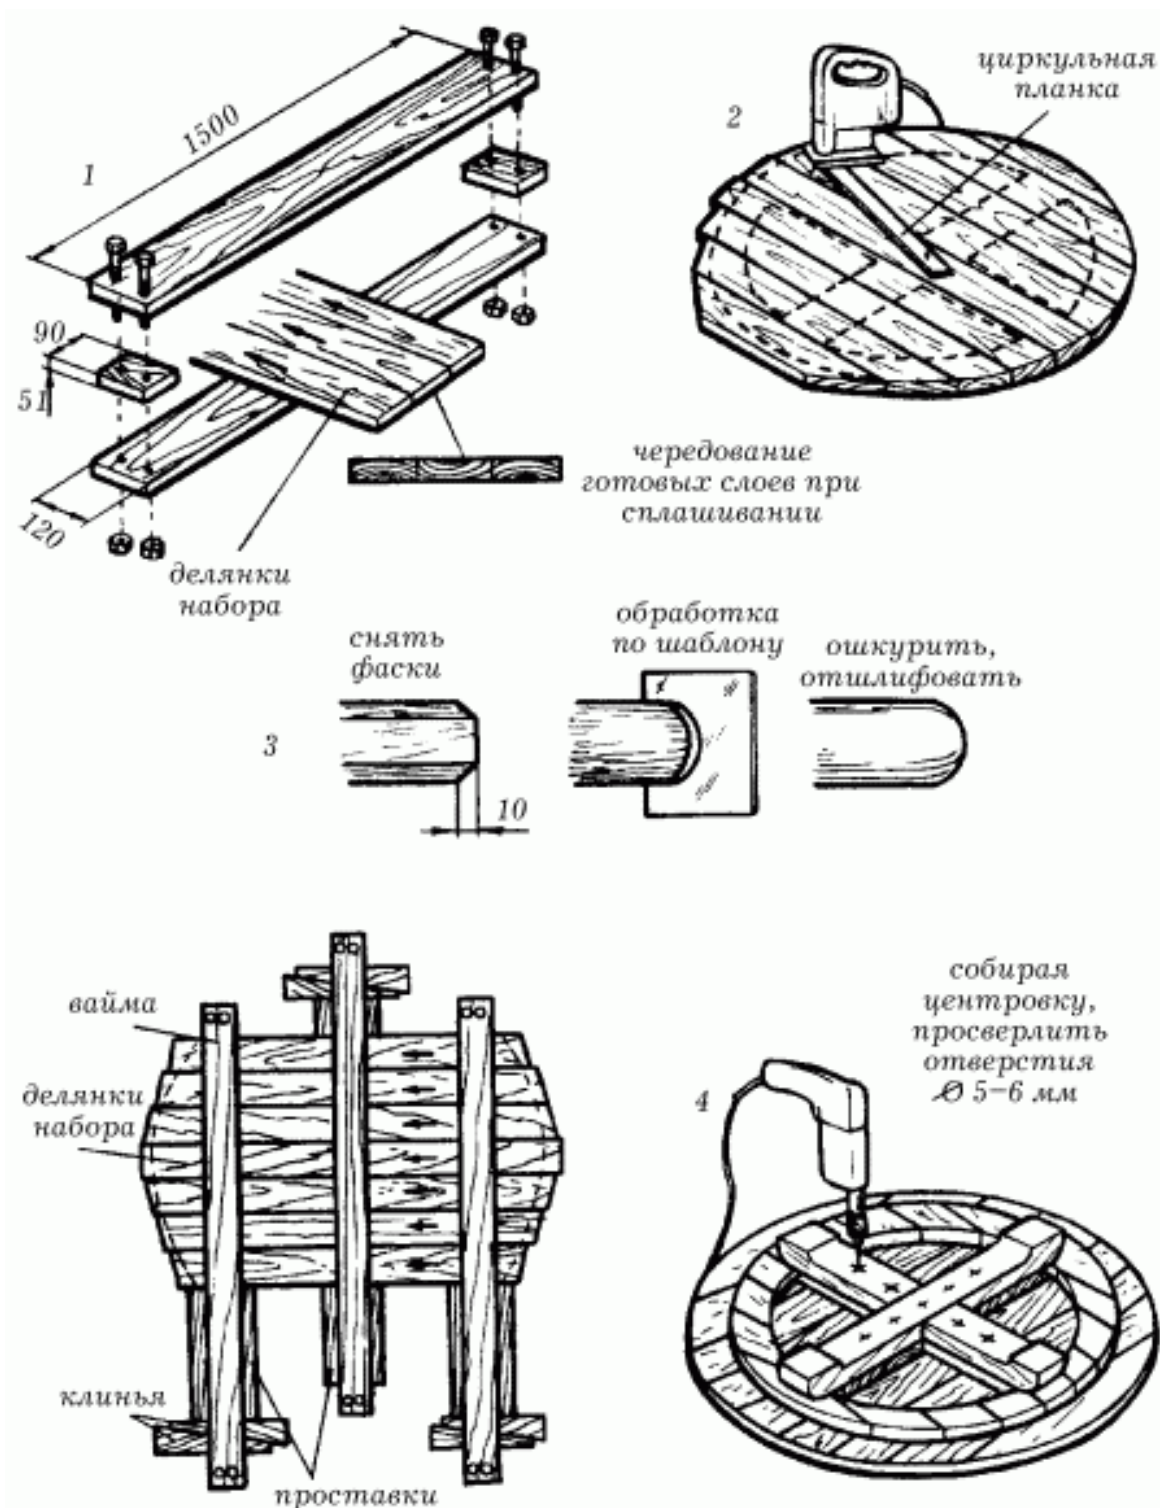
Изготовление стола из массива древесины: 1 – набор заготовки столешницы; 2 – выпиливание круговой заготовки; 3 – строгание кромок столешницы; 4 – высверливание отверстий под ножки.
